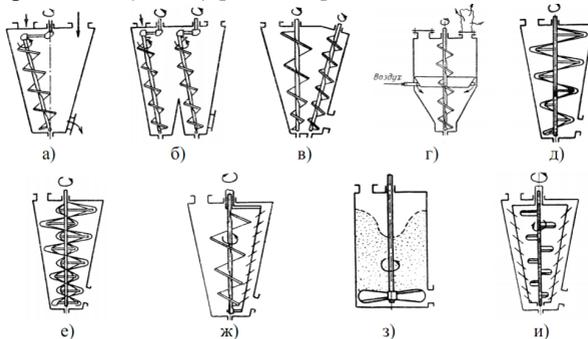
Конструктивные схемы смесителей с вертикальной рабочей камерой
